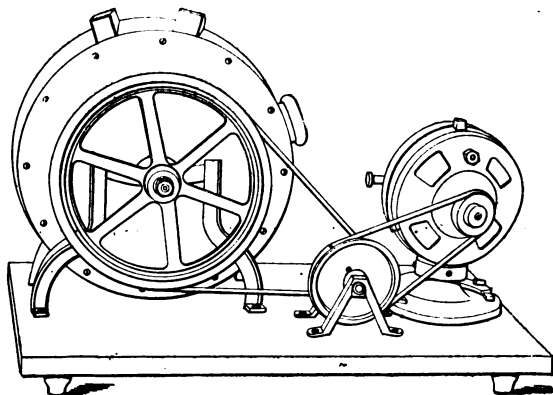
Machine à nettoyer les couteaux commandée par un moteur électrique.
